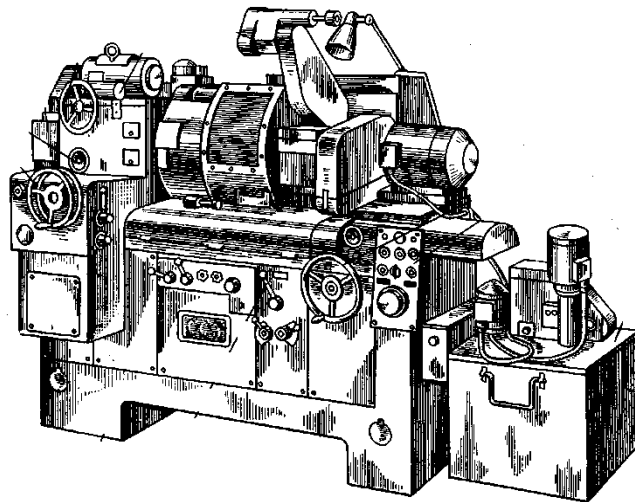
Універсальний внутрішньо-шліфувальний верстат 3A227
